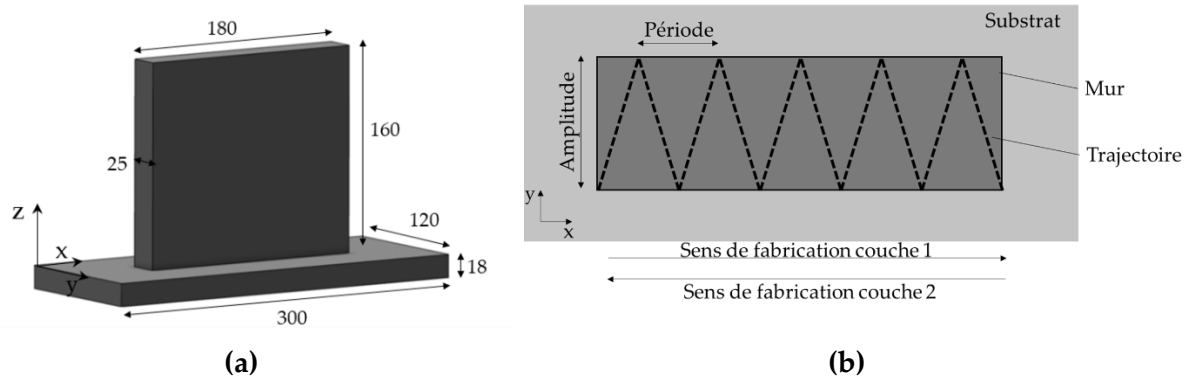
Dimensions du mur et trajectoire de fabrication en vue isométrique (a) et vue de dessus (b)
